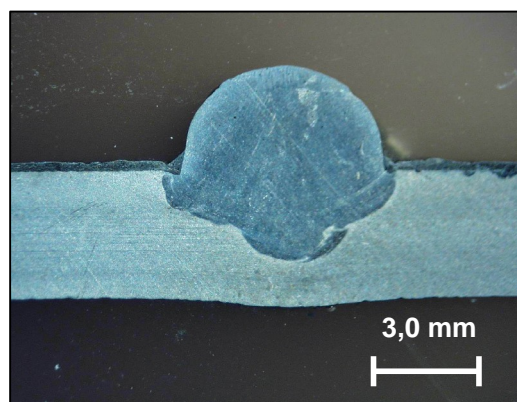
Macrografia de seção transversal de cordão de solda com eletrodo revestido AWS E309L sobre revestimento aspergido com arame AWS E309L por AS com espessura de 0,21 mm. Energia de soldagem 6,5 kJ/cm (70 A, 26 volts, 17 cm/min). Ataque Villela.
